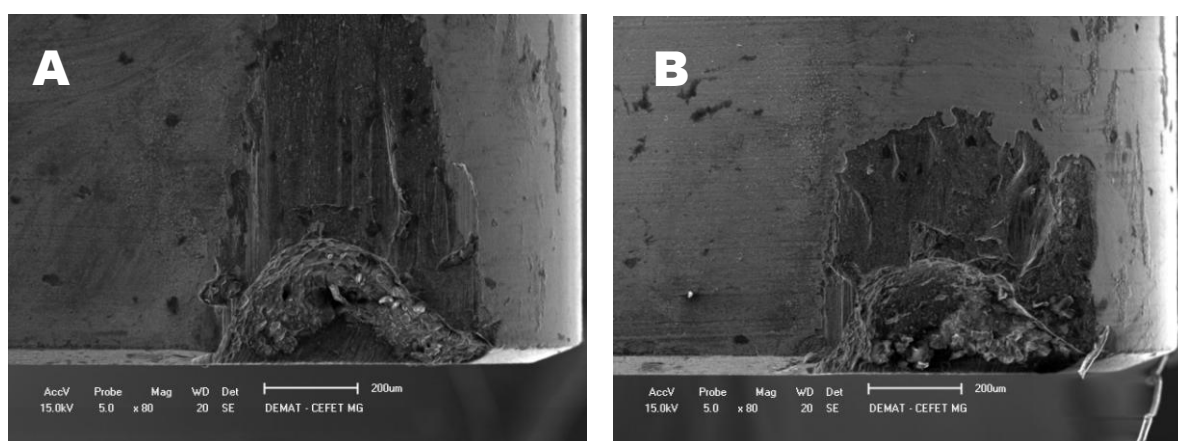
Fotografia MEV do desgaste da ferramenta de PcBN CB7050 com fluido de corte por jorro com $v_c = 450\text{m/min}$. (A) $f = 0,08\text{mm/rot}$; (B) $f = 0,12\text{mm/rot}$.
